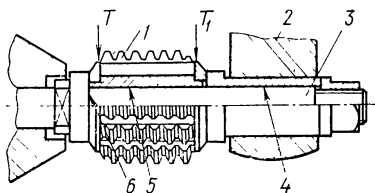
Правильная установка и зажим червячной фрезы на оправке зубофрезерного станка
